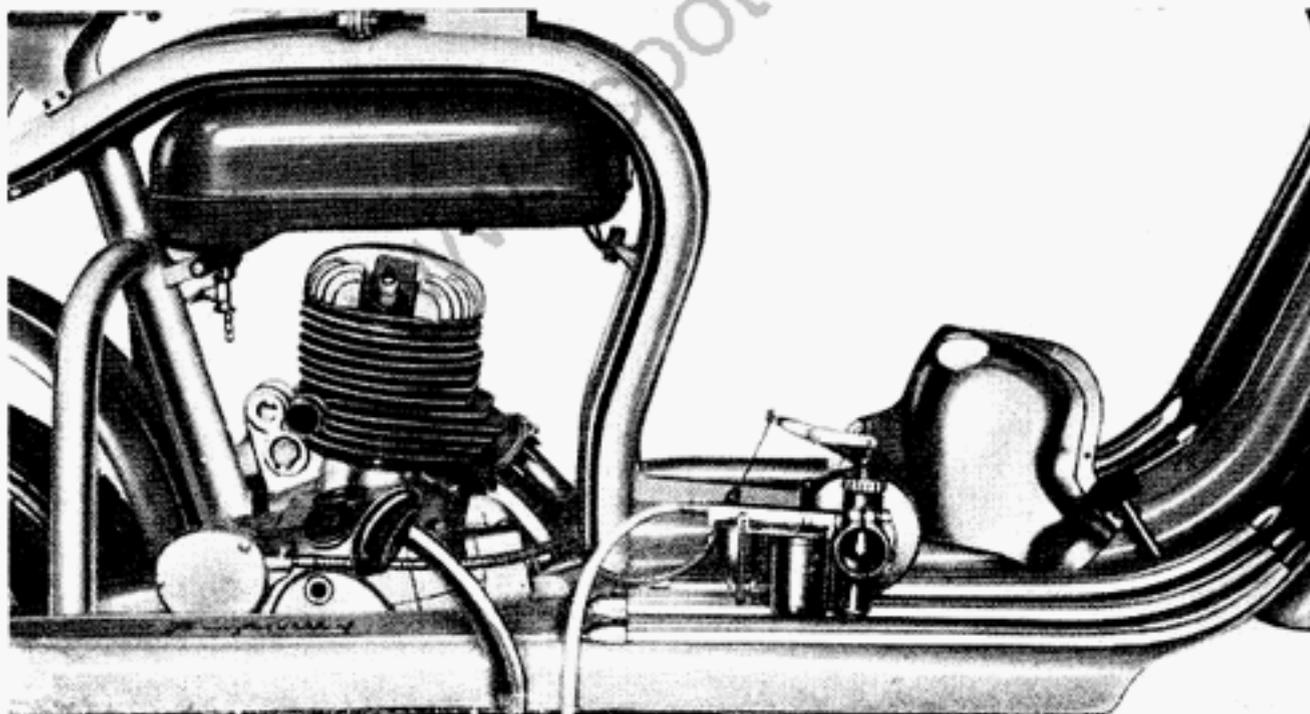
Smontaggio serbatoio, carburatore e testa cilindro.
